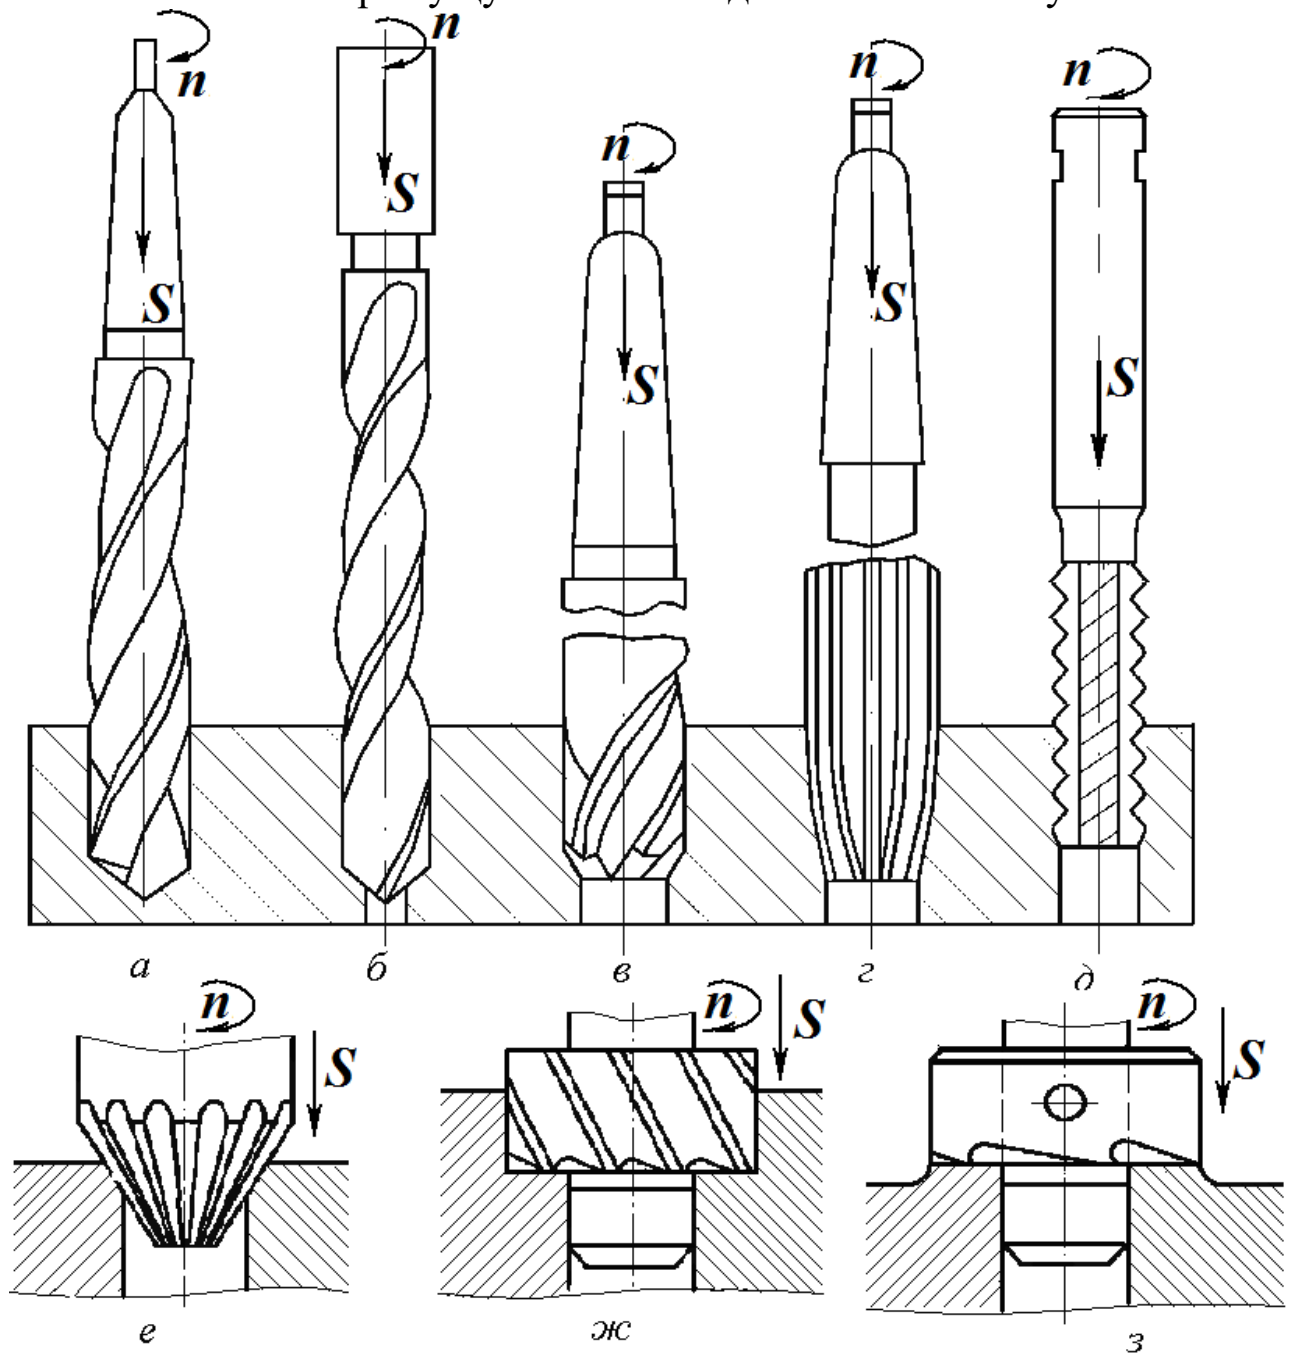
Схемы обработки заготовок на вертикально-сверлильных станках
